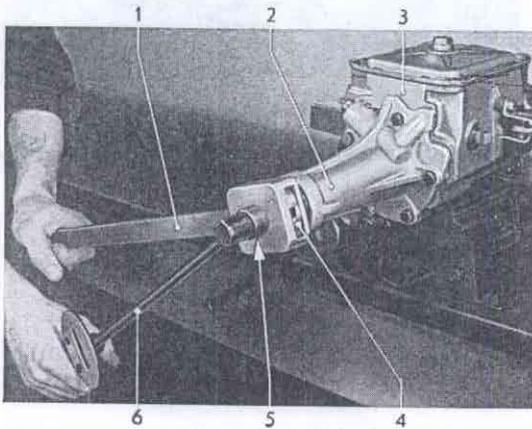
Getriebehauptwellenflansch abschrauben – Bild zeigt Vorgang beim Befestigen
